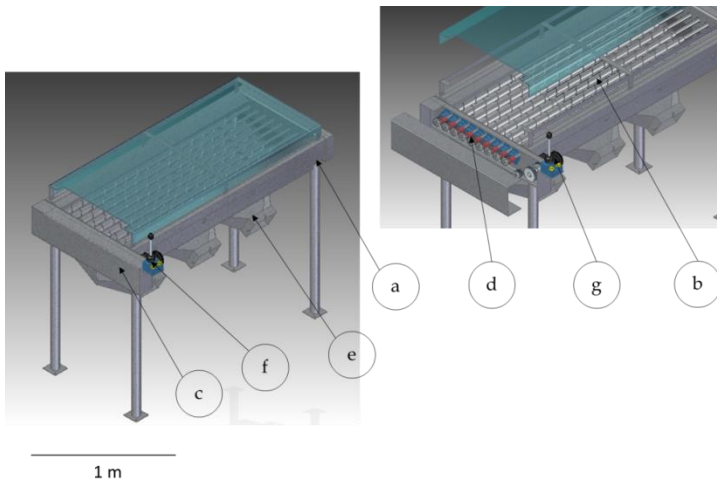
Modelo gráfico da máquina classificadora de mexilhões: a – chassi; b – eixos escalonados helicoidais; c – cabeçote; d - cadeia cinemática de correia e polias sincronizadoras; e – calha compartimentada; f - válvula direcional de alavanca; g - motor hidráulico.
